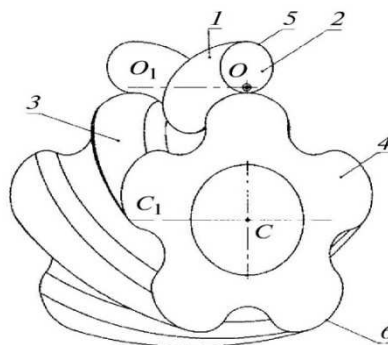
Поверхности зубьев колеса идеального зацепления [20]
